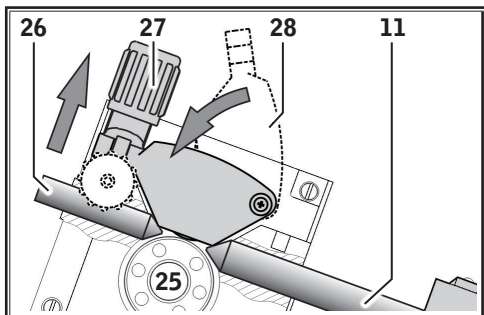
Закрывать 2-роликовый механизм подачи проволоки
